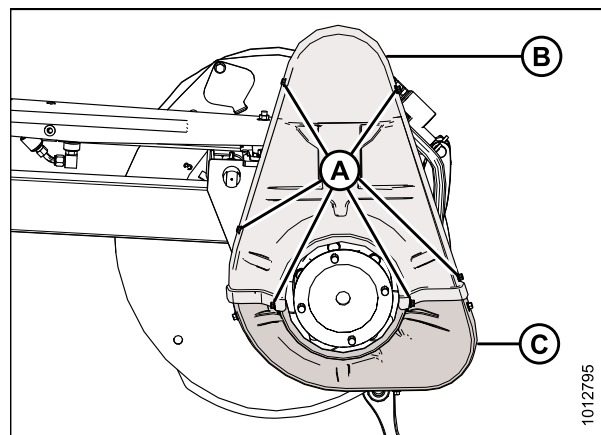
Крышка привода — сдвоенное мотовило
